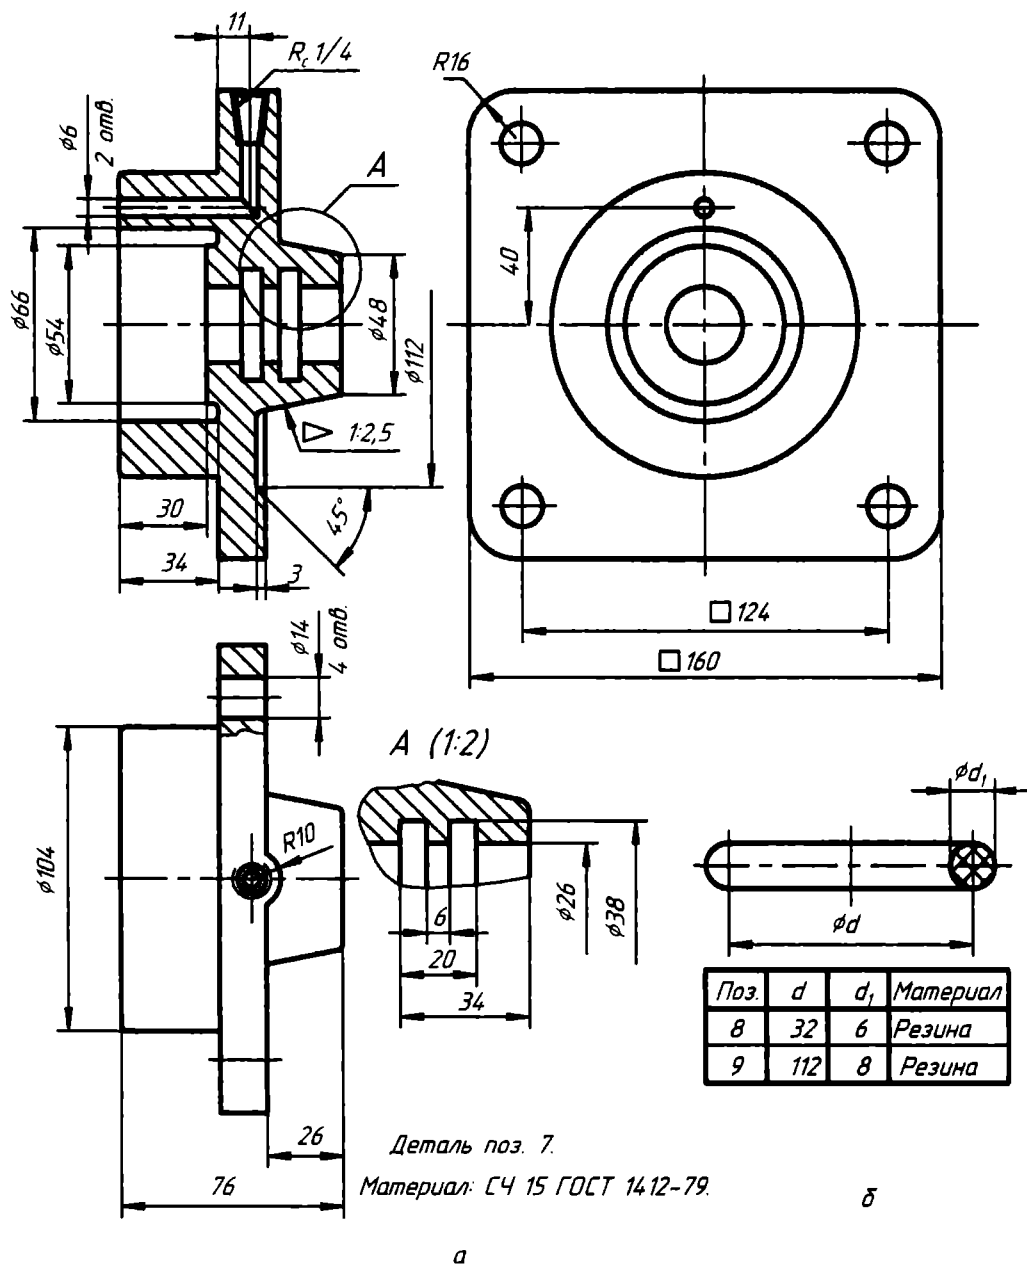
Чертежи: а — крышки правой; б — уплотнительных колец
